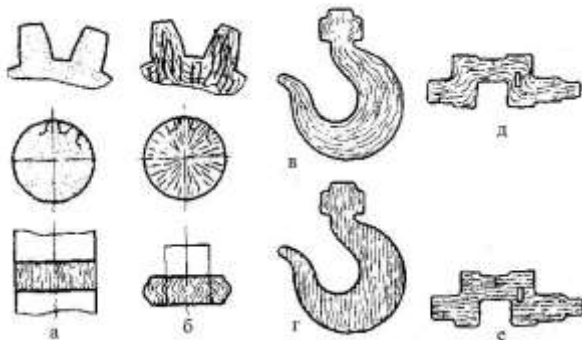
Вплив перерозподілу волокон у металі після обробки тиском : а, г, е – неправильно (лише шляхом механічної обробки заготовки); б, в, д – правильно (шляхом попереднього пластичного деформування заготовки)
